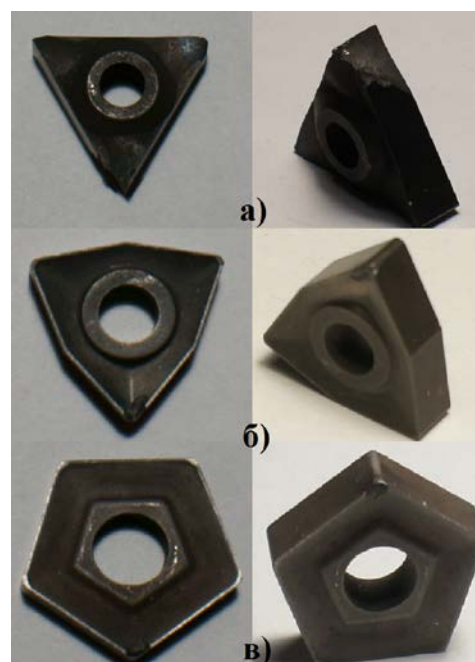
Неперетачиваемые твердосплавные пластины после экспериментальных исследований: а - TNUM 220404ТК (причина выхода из строя - излом режущей кромки); б - WNUM 02114 (скол режущей кромки); в - PNUM 11048Н30 (износ режущей кромки)
